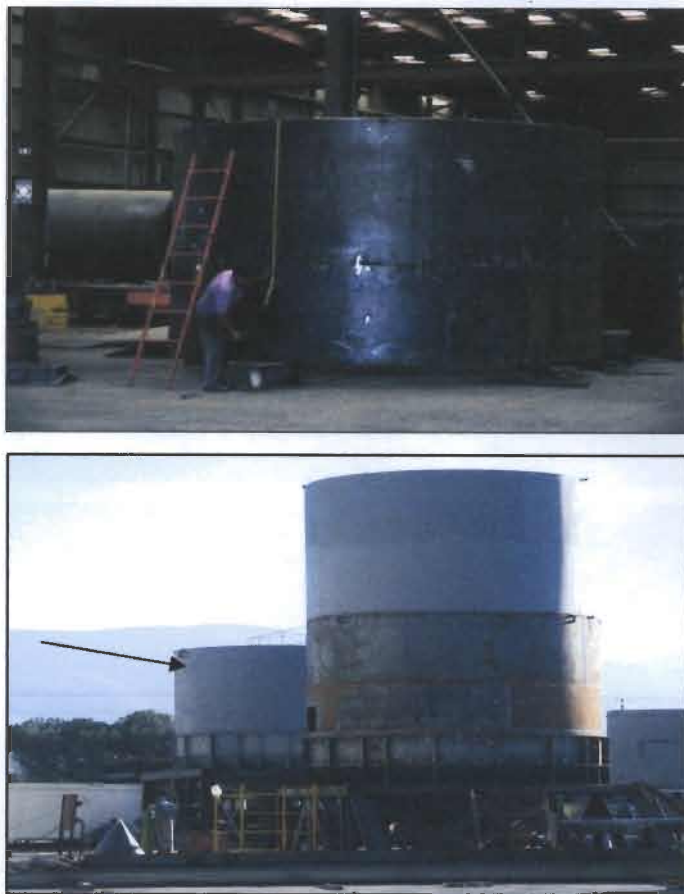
Medición de un componente para su transporte y futuro ensamble fuera de planta.
